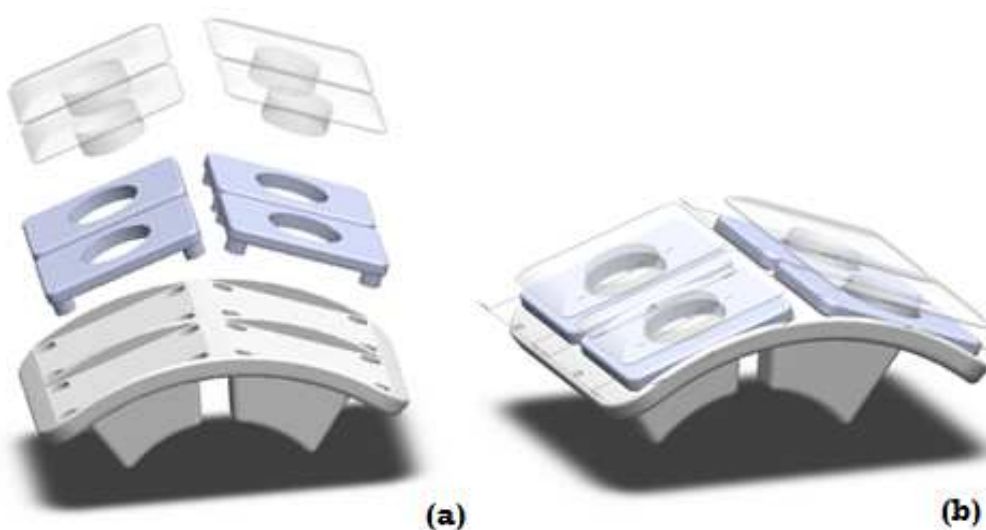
Conjunto mecânico na posição de montagem (a) e montado (b)
